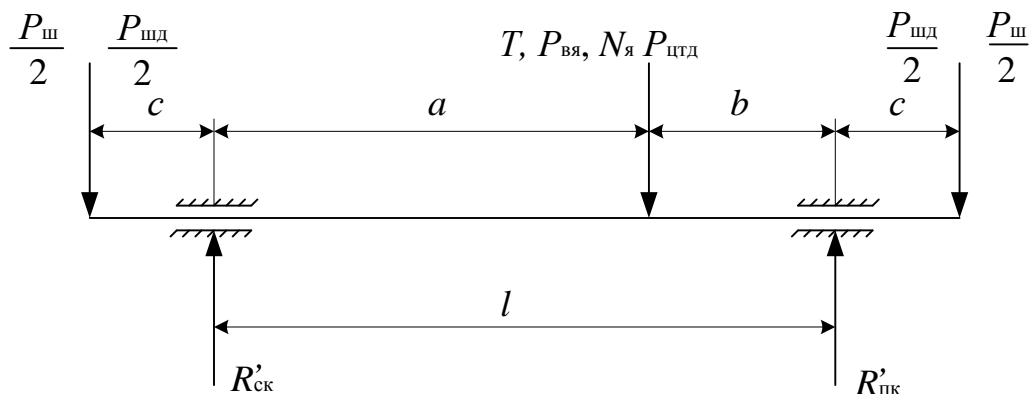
Расчетная схема нагружения вала якоря тягового двигателя с двусторонней зубчатой передачей
